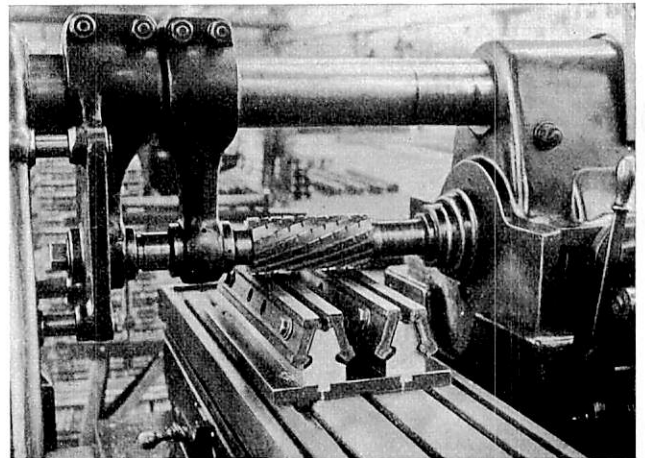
Aufspannvorrichtung zum Fräsen von Laschen.
